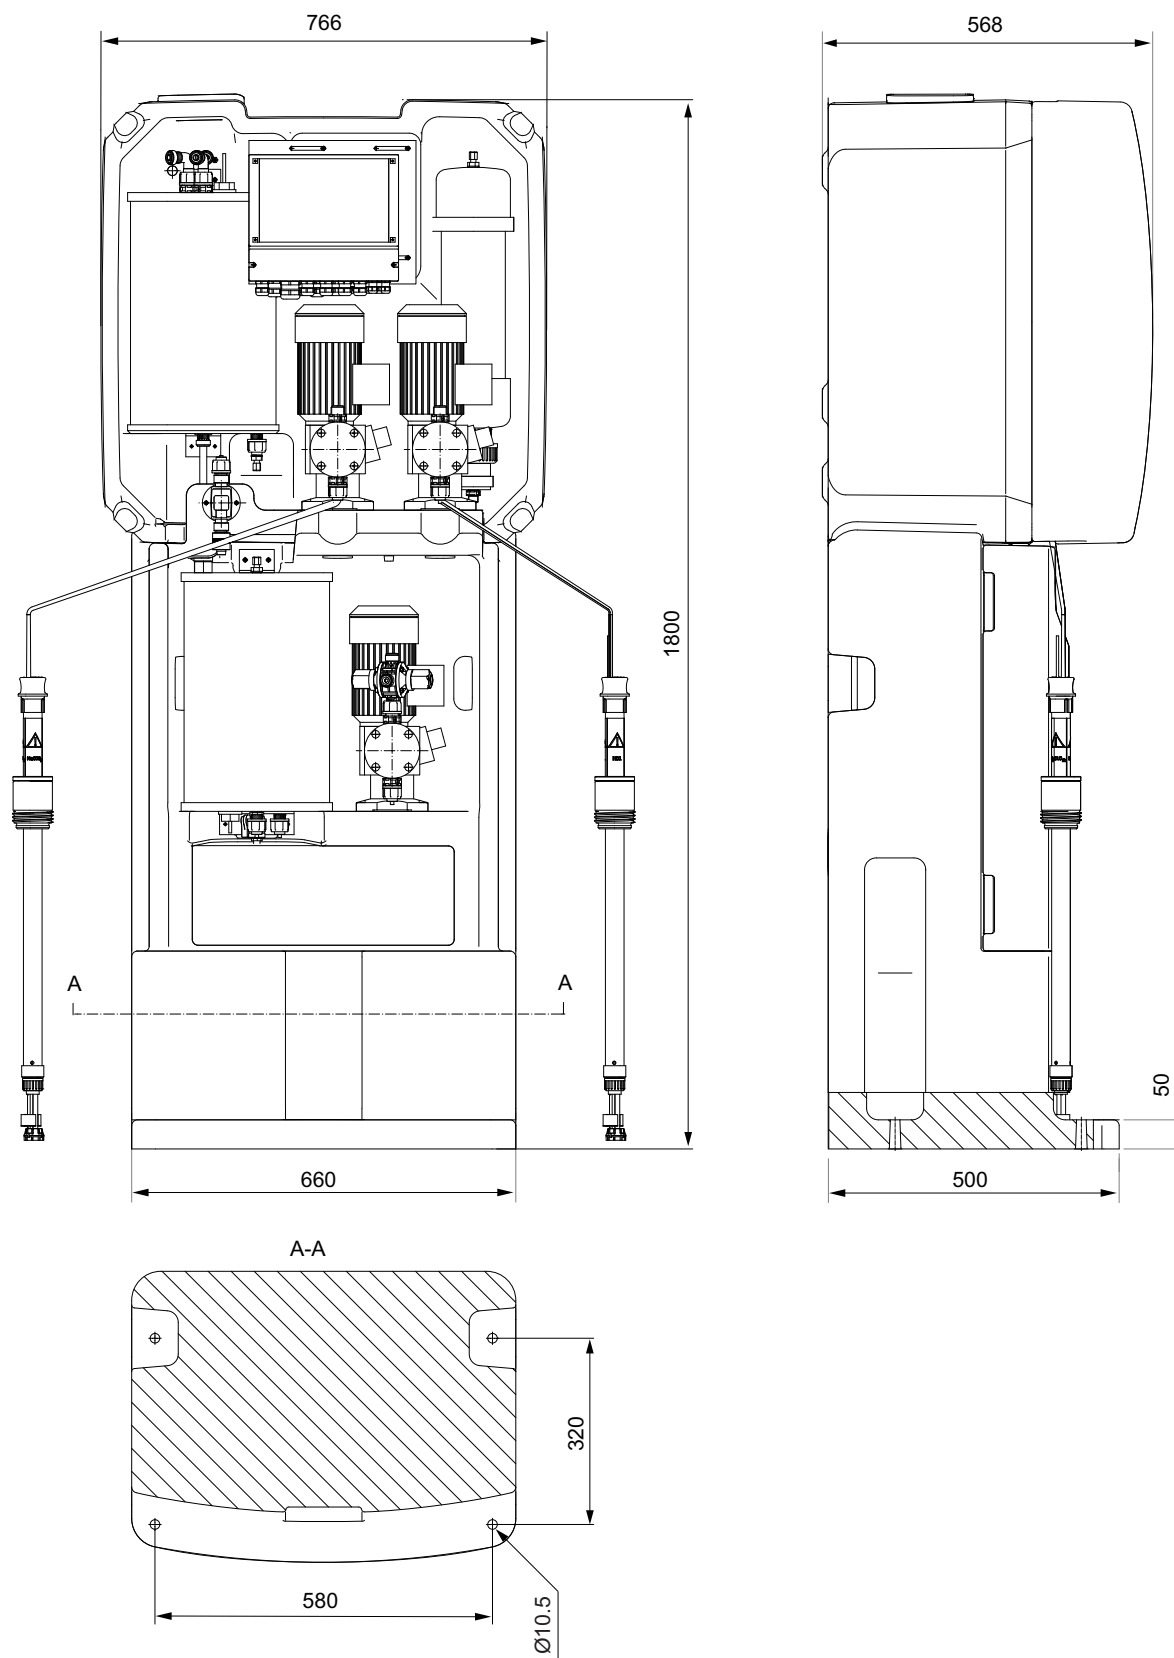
Габаритные размеры установки Oxiperm Pro OCD-162-30 и OCD-162-60, с указанием отверстий для крепления
